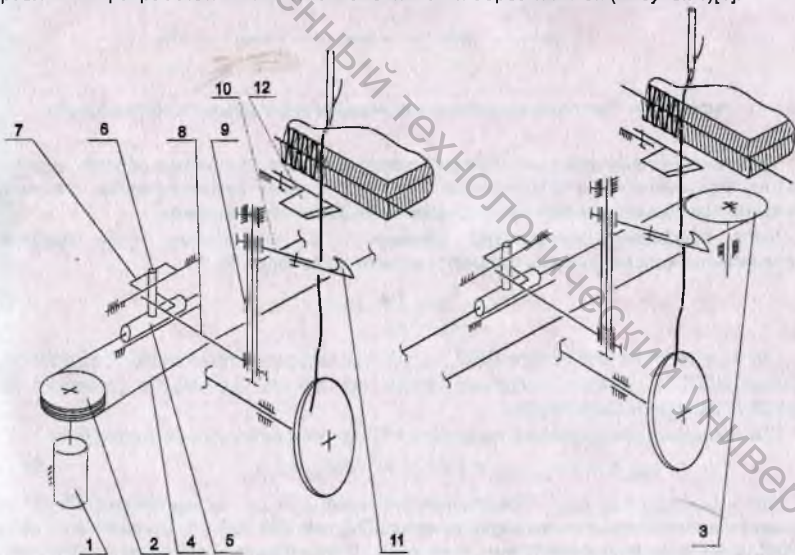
Кинематическая схема механизма автоматической обрезки ниток
